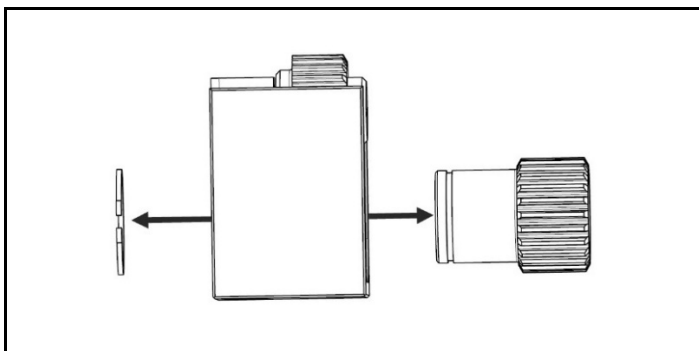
Fjern drivhjulets sikringsbøjle og drivhjulet
